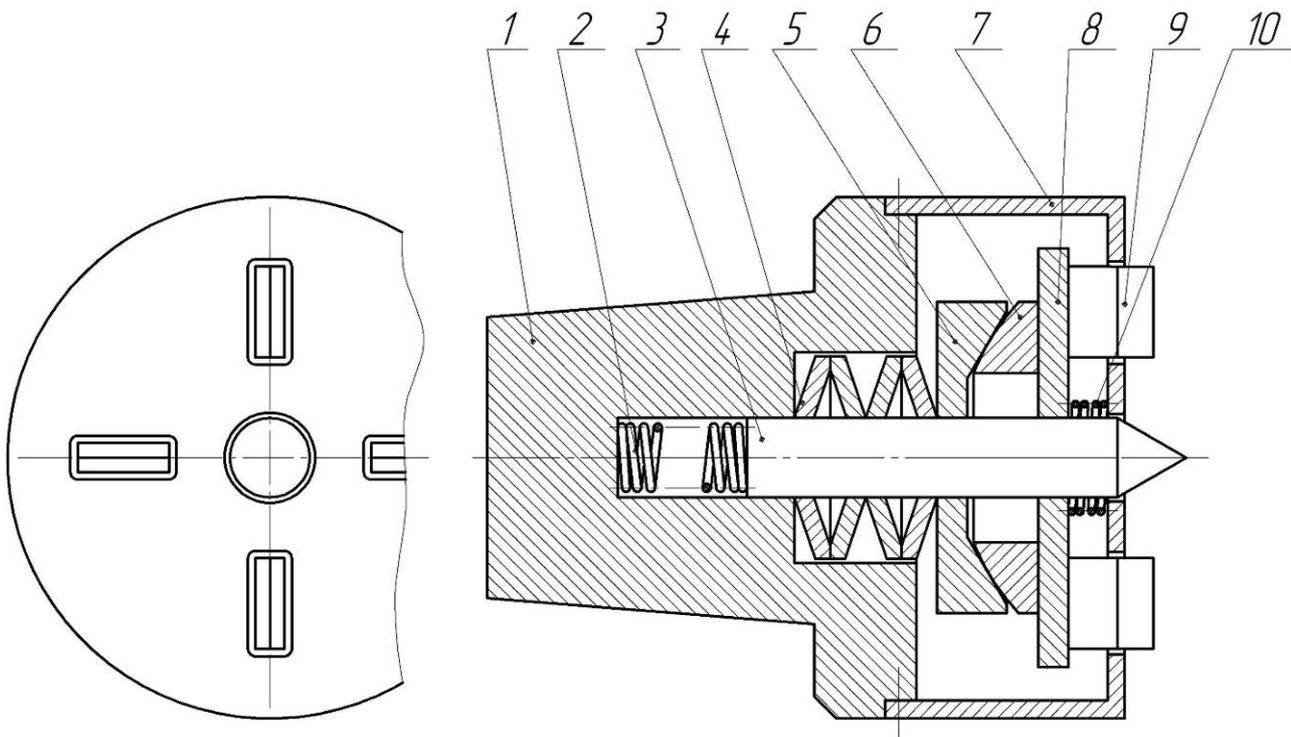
Поводковое устройство со стопорением плавающего центра тарельчатыми пружинами [10]
